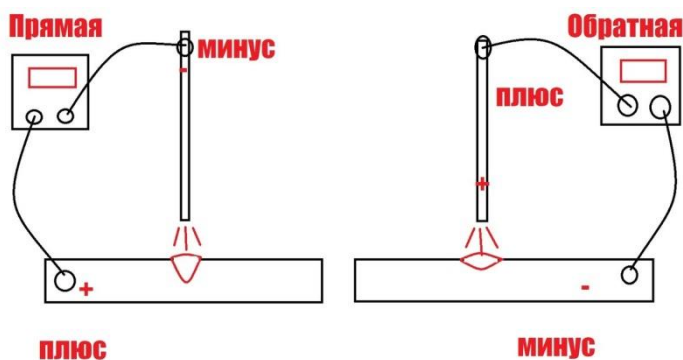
Подключение источника сварочного тока при прямой и обратной полярности
